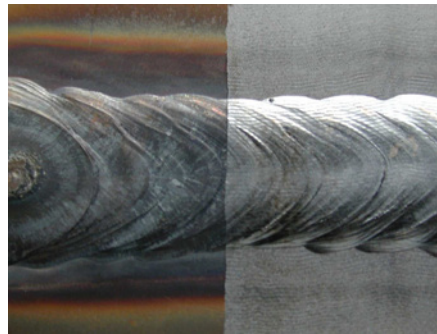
Laserreinigung einer Schweißnaht
